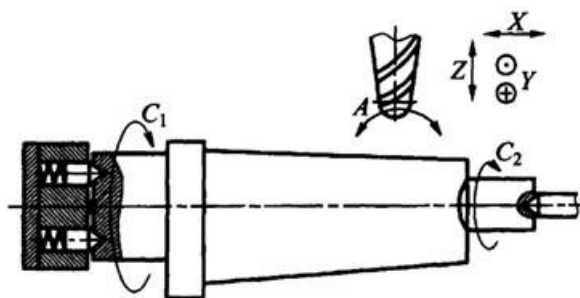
Схема руху інструмента й заготовки при фрезеруванні профілю пера (варіант 2).
